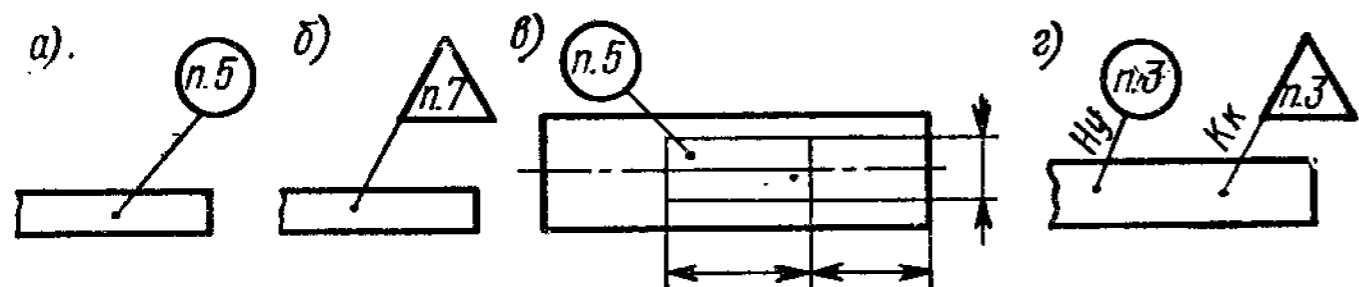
Нанесение на чертеже маркировки и клейма
